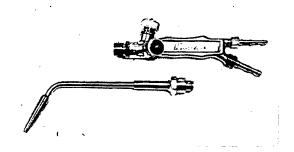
Wechselschweißbrenner in Leichtmetallausführung (Weber-Werke Siegen)
